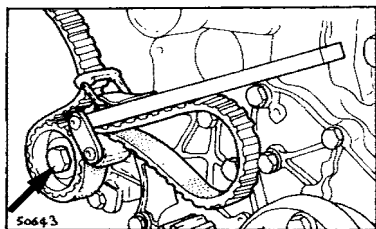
Использование приспособления Renault для удерживания зубчатого шкива промежуточного вала
